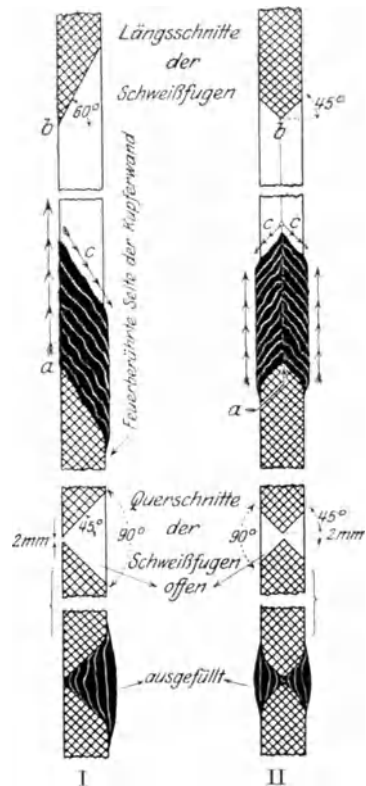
Gang der Schweißung einer Fuge, welche in einer senkrechten Wand von unten nach oben verläuft: I von einer Seite, II von beiden Seiten.
